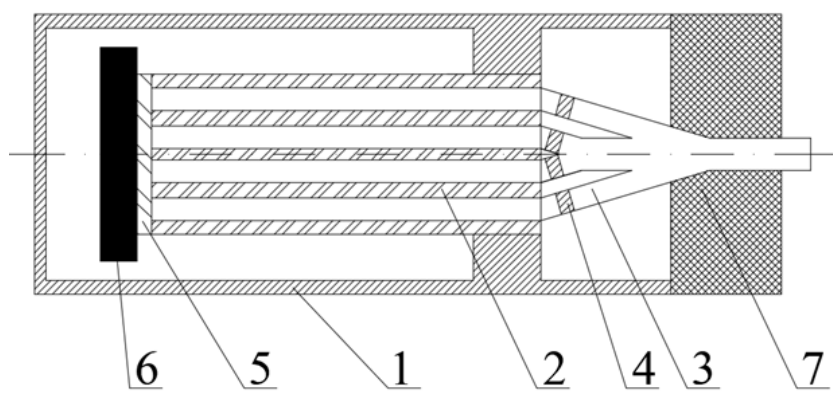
Волоконно-оптичний інклінометр: 1 – корпус; 2 – світловод револьверного типу; 3 – багатогілковий розгалужувач; 4 – оптичні фільтри; 5 – віддзеркалюючий шар; 6 – інерційна маса; 7 – вібропоглинаюча захисна прокладка
